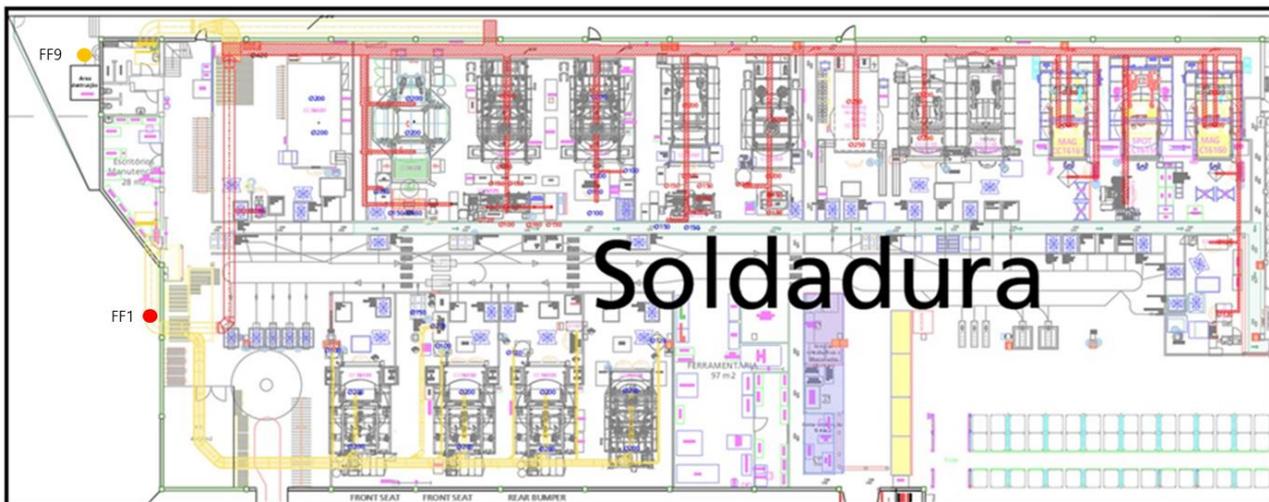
Detalhe do layout da soldadura em vigor após 2017
